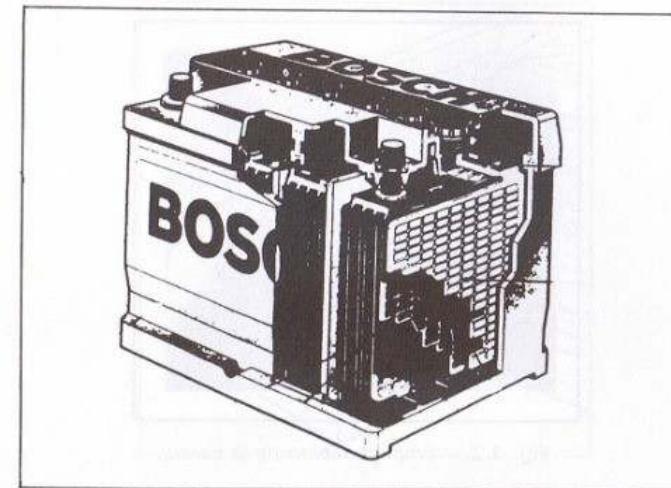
Batería seccionada, mostrando las placas de un elemento.
